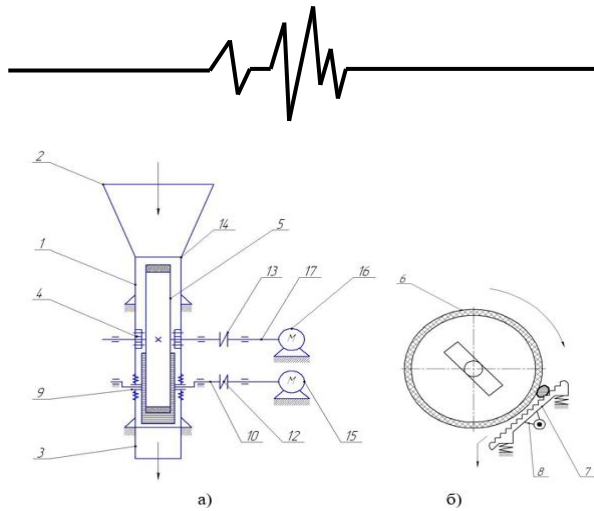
, а) – принципова схема вібраційного обладнання для лущення волоського горіха з кінематичним віброприводом, б) – робочі органи обладнання: 1 – корпус; 2 – завантажувальний бункер; 3 – розвантажувальна горловина; 4 – варіативний механізм; 5 – дробильне колесо; 6 – гумове покриття; 7 – підпружинене рифлене деко; 8 – опори; 9, 11 – підшипникові вузли; 10 – кінематичний віброзбудувач; 12, 13 – еластичні муфти; 14 – шиберна заслінка, 15, 16 – електродвигуни; 17 – приводний вал дробильного колеса
